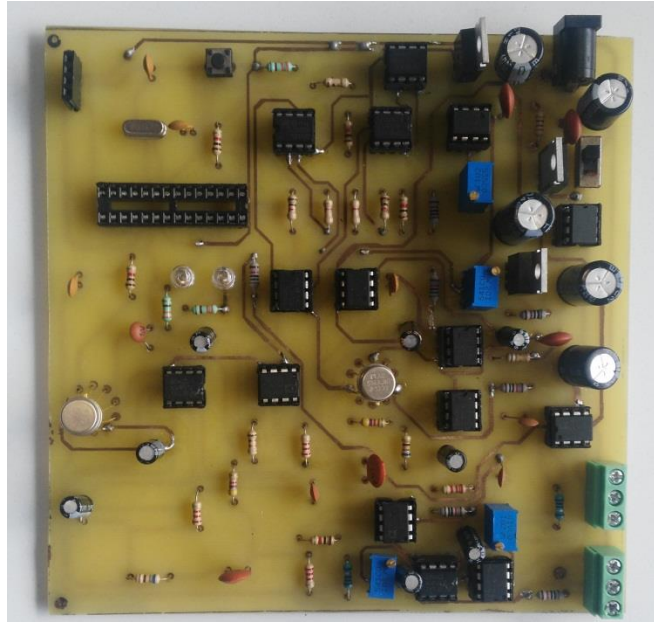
Tarjeta de adquisición de señales mioeléctricas, diseñada en PCB [22].
